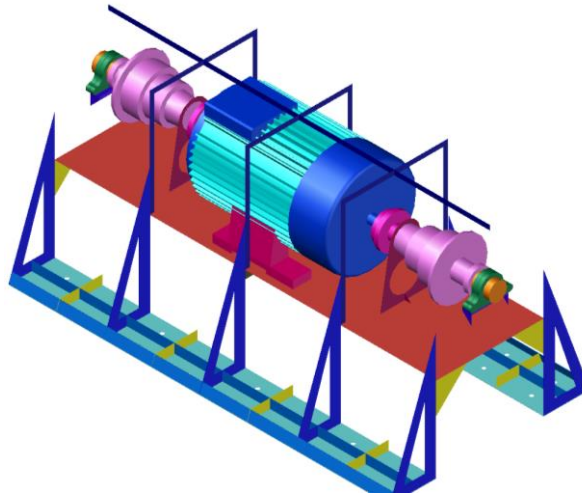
Detalle del modelado de los refuerzos de la estructura.
